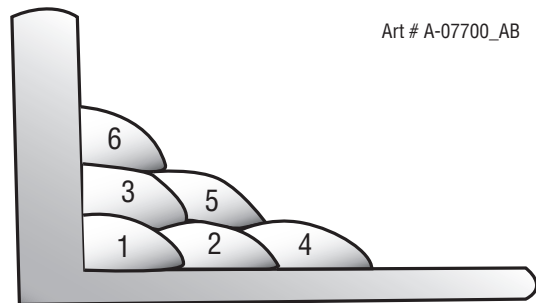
Varios recorridos en la soldadura de perfil en ángulo HV
